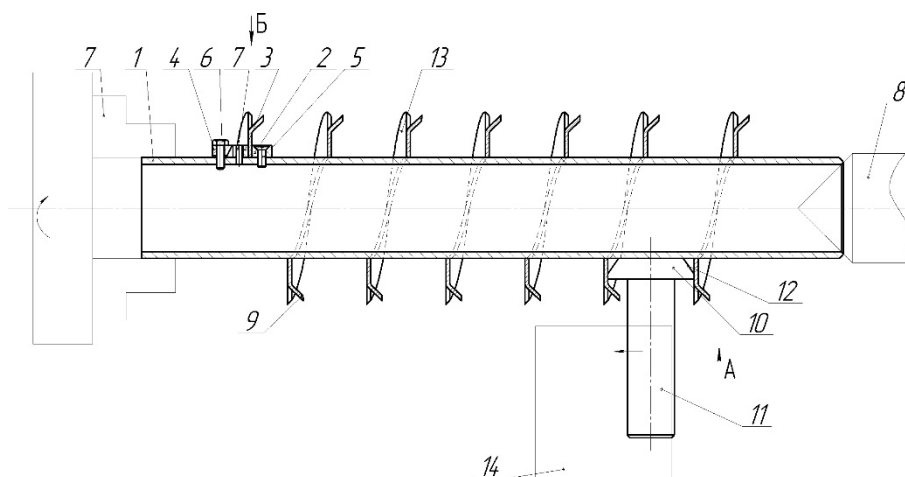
Схема калібрування шнека з виготовленими ножами-подрібнювачами
